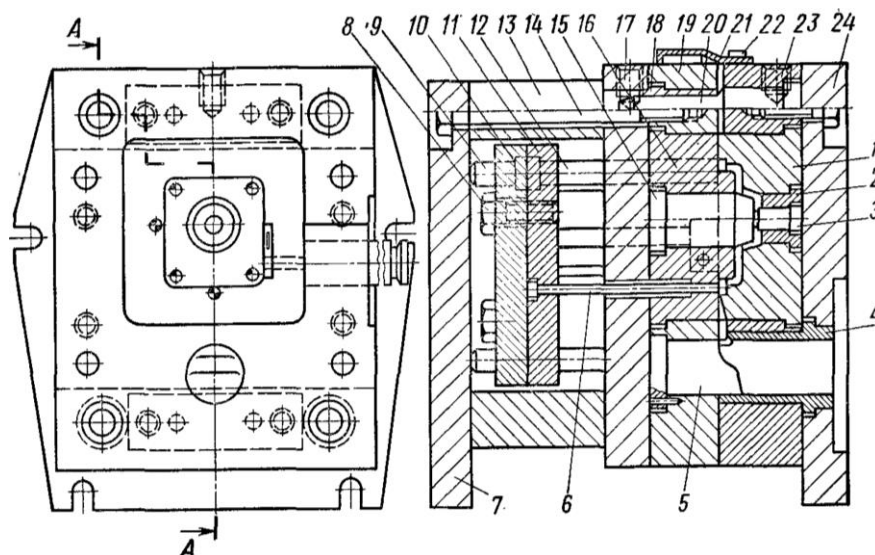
Конструкция пресс-формы для литья под давлением
